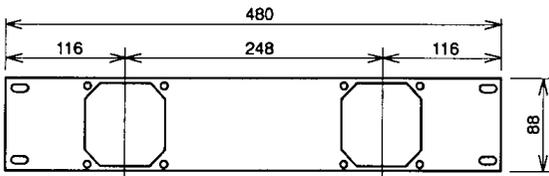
Rack-Einbau mit Kühlventilatoren und Lüftungsblenden
